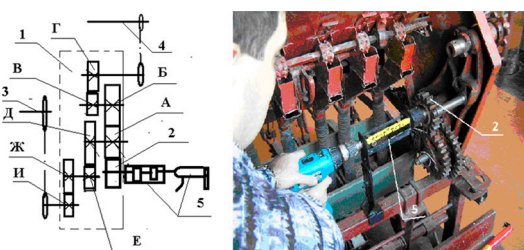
Схема присоединения устройства к редуктору сеялки: 1 – редуктор зерновой сеялки; 2 – зубчатка устройства; 3 – вал зерновых аппаратов; 4 – вал туковывсевающих аппаратов; 5 – разработанное устройство привода; А – зубчатка редуктора, установленная на его первичном вале
